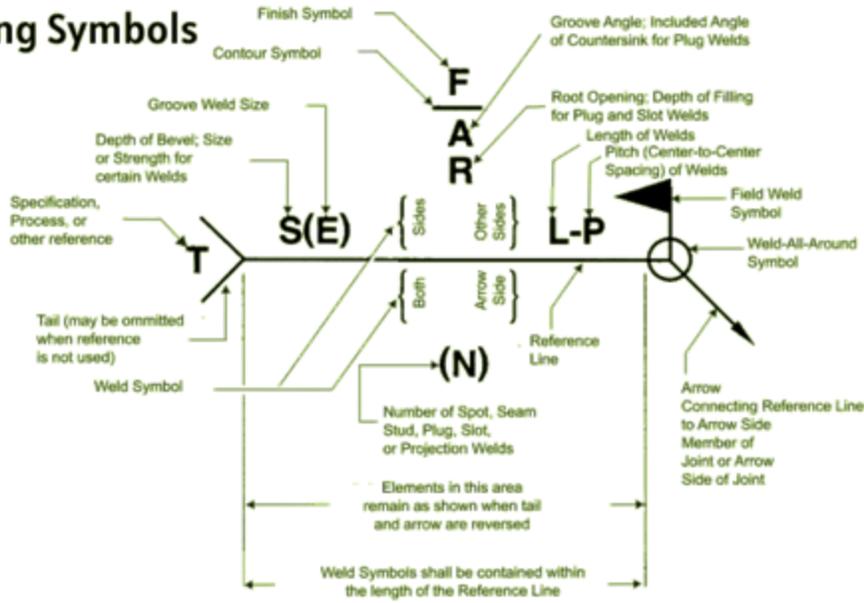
Símbolos de soldadura – A definir por Talleres Corral
